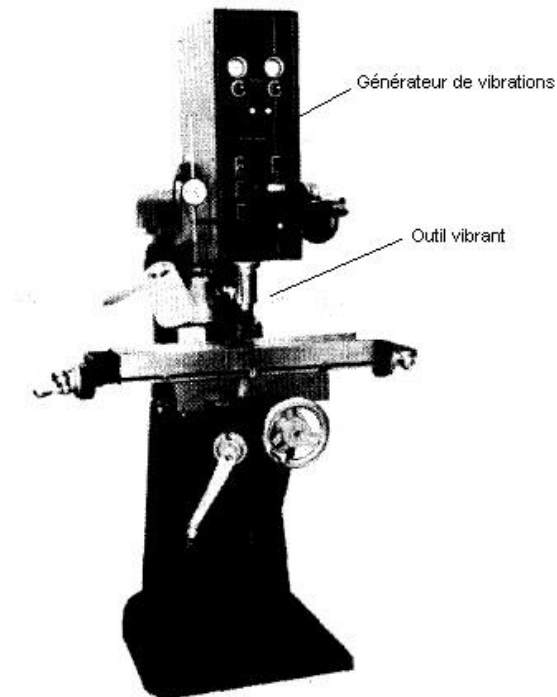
Photographie d'une fraiseuse avec usinage ultrasonique en 1975 [Sho75]. Cette fraiseuse a une vitesse de rotation de $5\,000\text{ tr.min}^{-1}$ et utilise une vibration axiale à 20 kHz combinée au mouvement rotatif. Le processus d'usinage ultrasonique est décrit comme une abrasion à haute vitesse et introduit une plus grande vitesse d'usinage, améliore la durée de vie de l'outil, réduit le chipping (écaillage) et améliore la précision. Parmi les applications, nous trouvons l'usinage de pièces pour réacteur nucléaire, l'usinage de céramiques ou de quartz.
